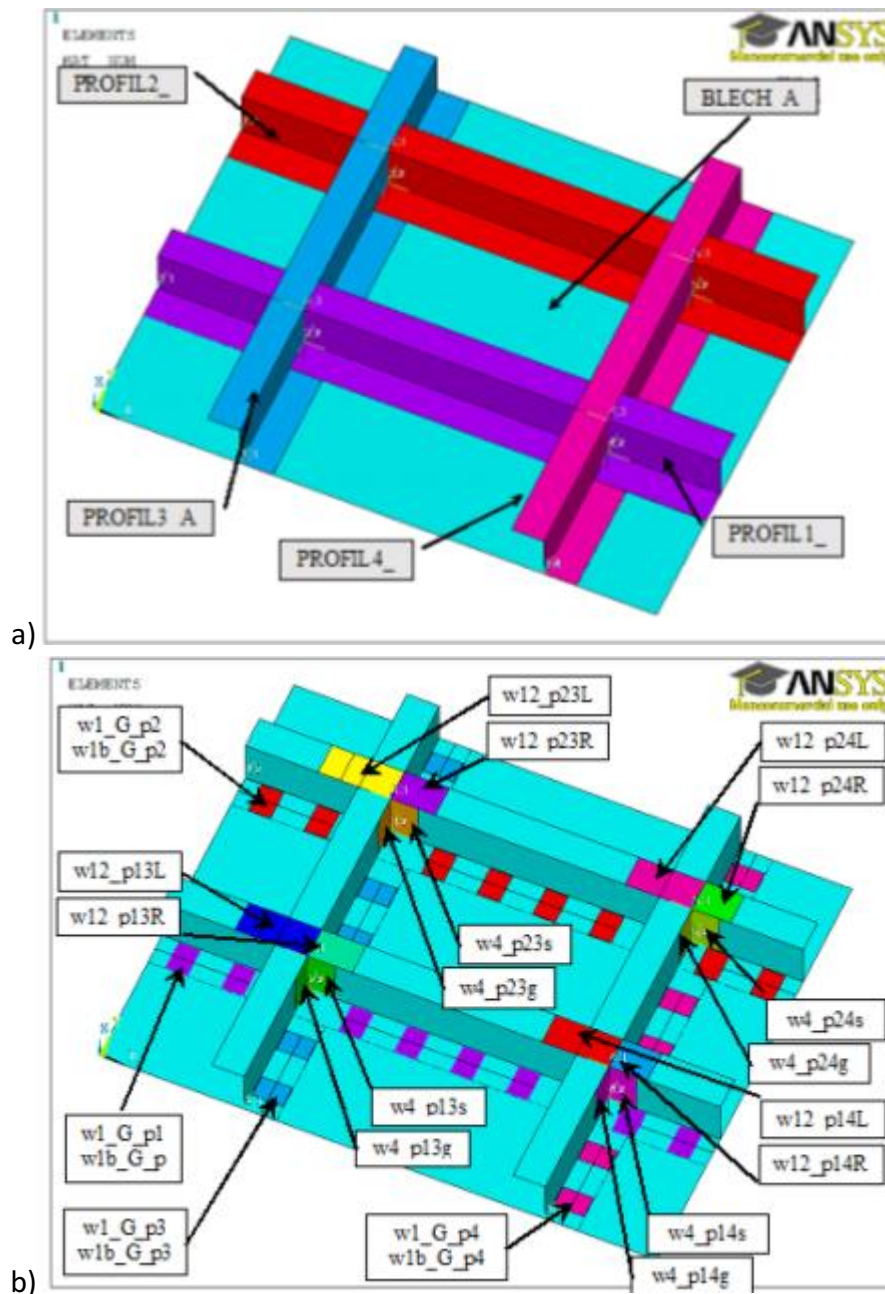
Schweißstruktur (Unterseite): a) Gruppe der Einzelemente; b) Berechnungsmodell mit einzelnen Schweißnähten
